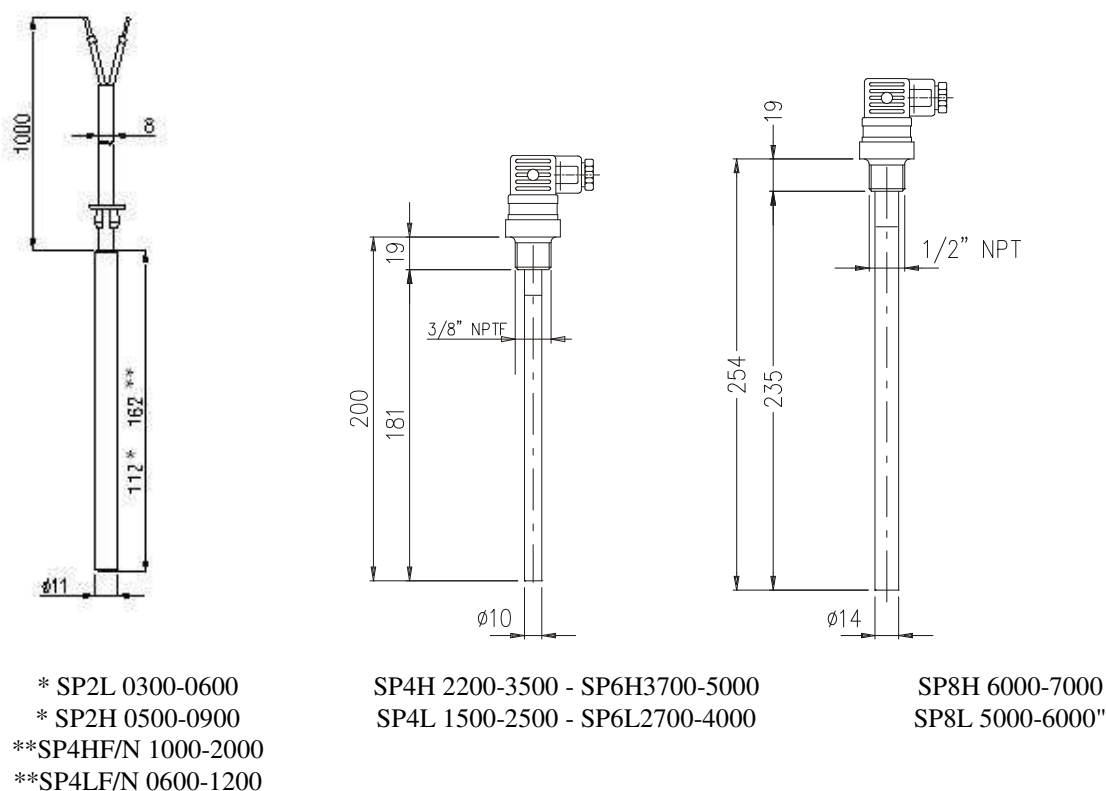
Габаритные размеры другого типа подогревателя картера
